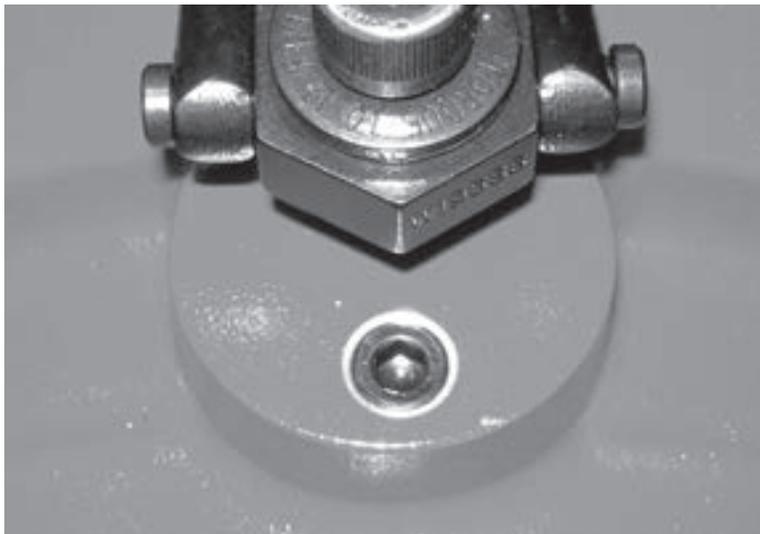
Inserte el tapón y atornille hasta que quede al ras con la parte superior de la carcasa.
